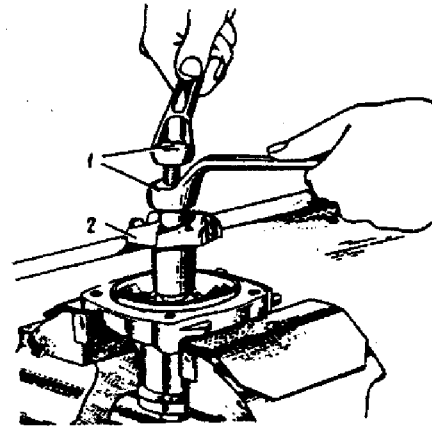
Remoção do rotor: 1 - extrator; 2 - rotor.
